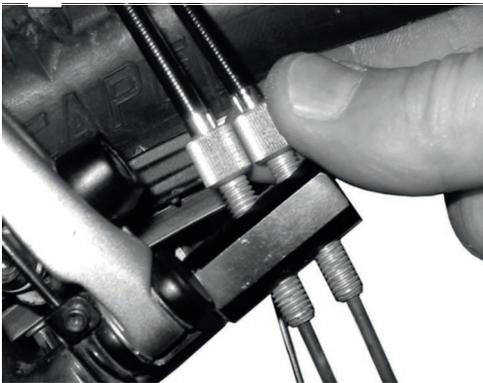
ROHLOFF-Naben Versionen mit interner Schaltansteuerung haben die Zugeinsteller am Zuggegenhalter
